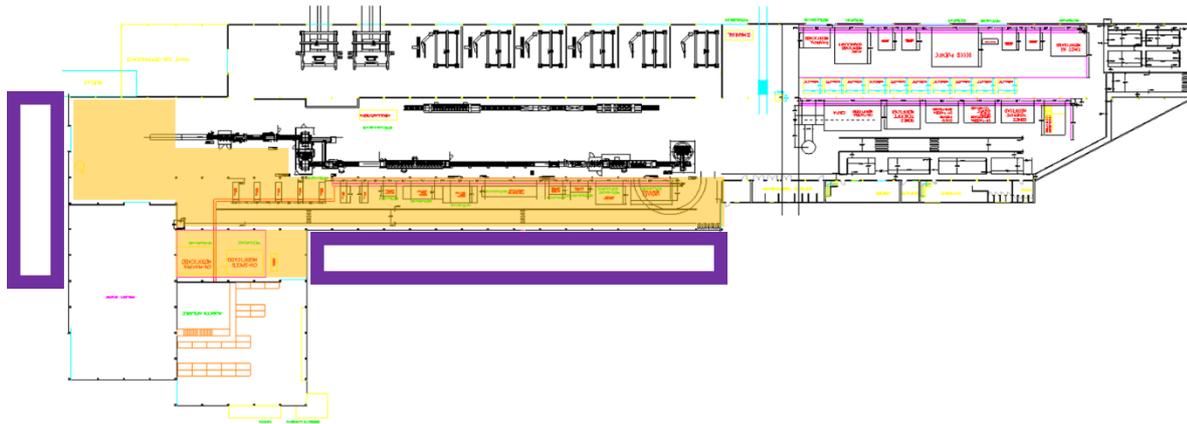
Sección de Elaborado. (PIEDRA NATURAL SL, 2016)
